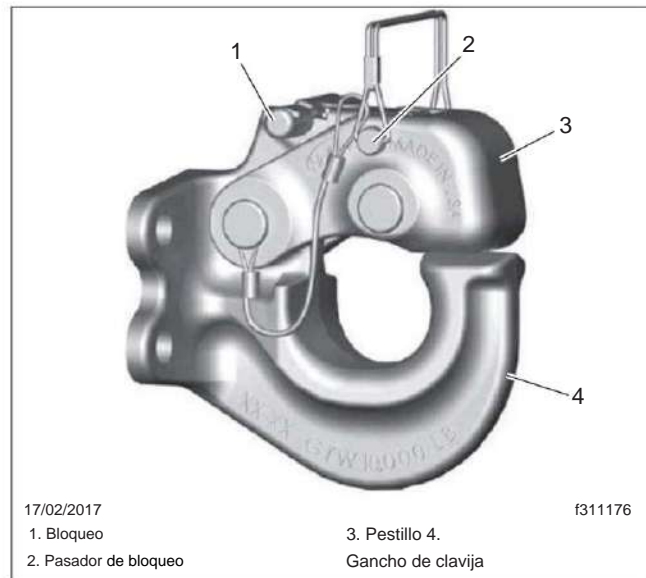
, Acoplamiento de remolque Holland con pasador de seguridad
